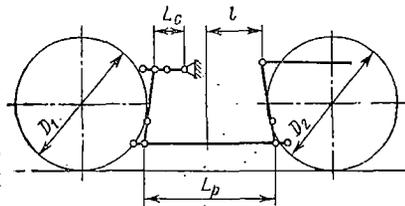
Схема установочных размеров рычажной передачи тележки грузового вагона при регулировке
